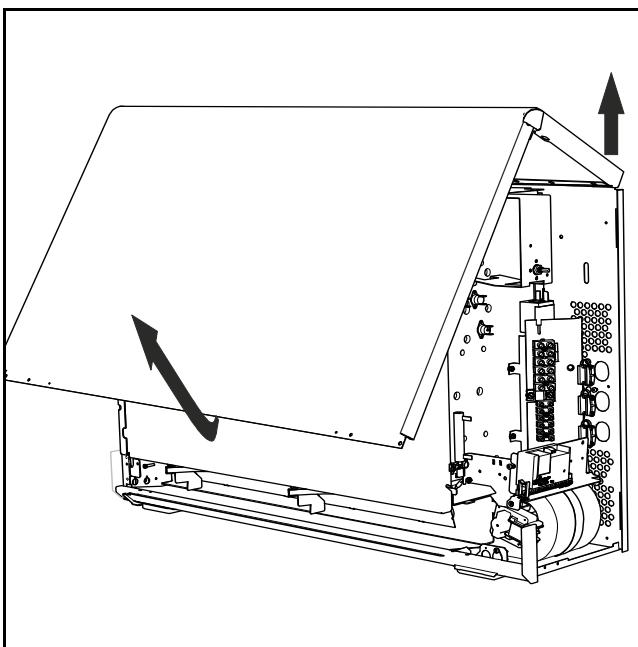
Spostare in avanti la parete anteriore sollevandola leggermente ed estrarla dagli elementi di fissaggio posteriori.
